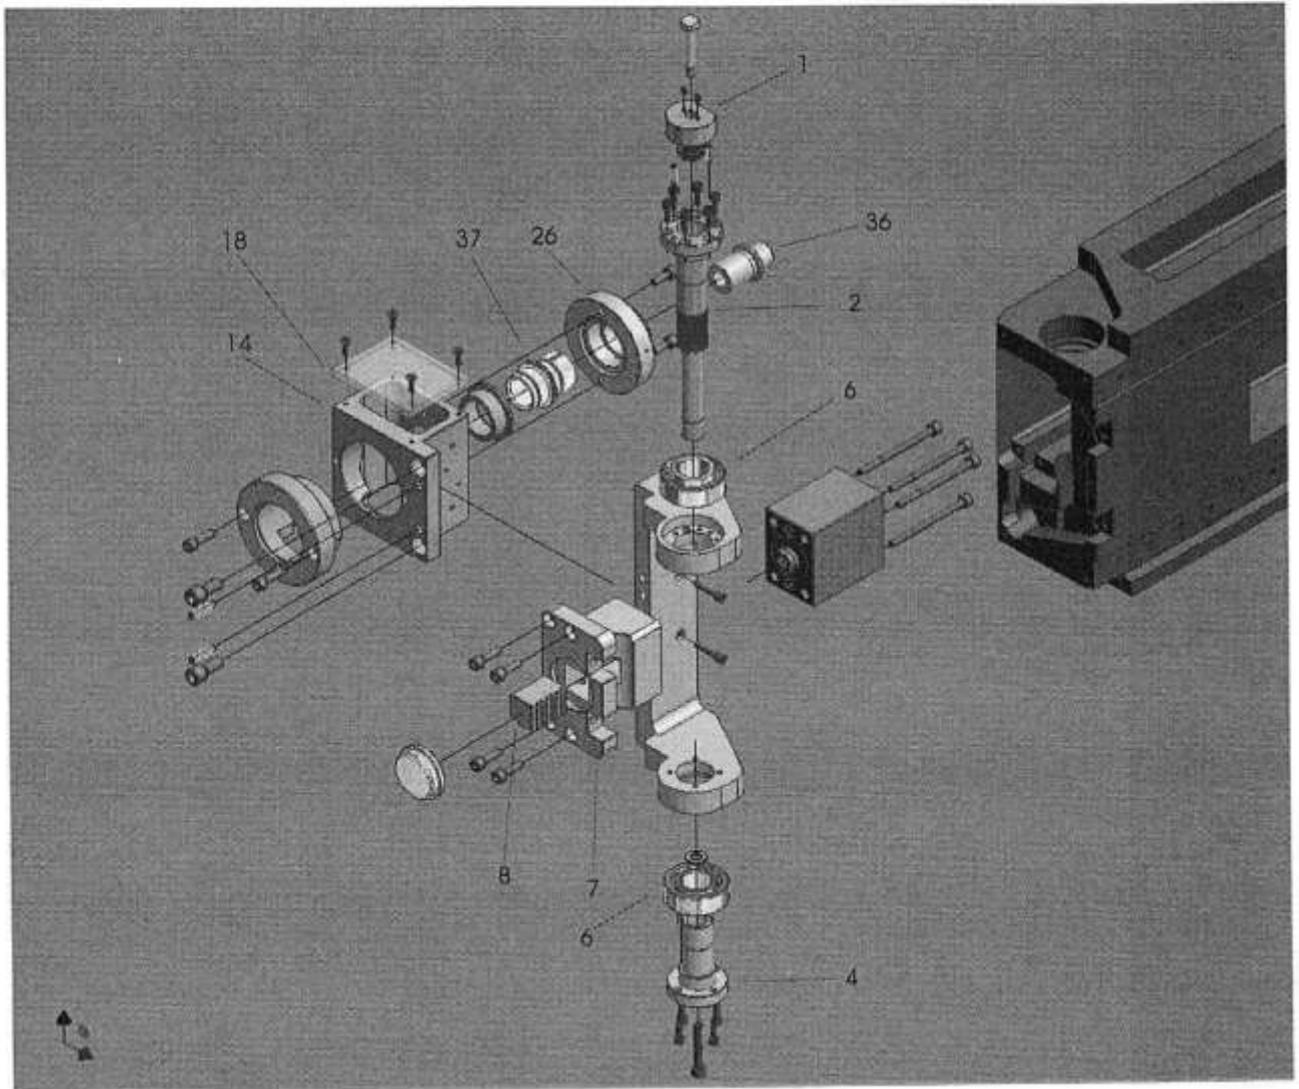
Bohrbuchsenhalter, Explosionszeichnung (Legende - nächste Seite)
